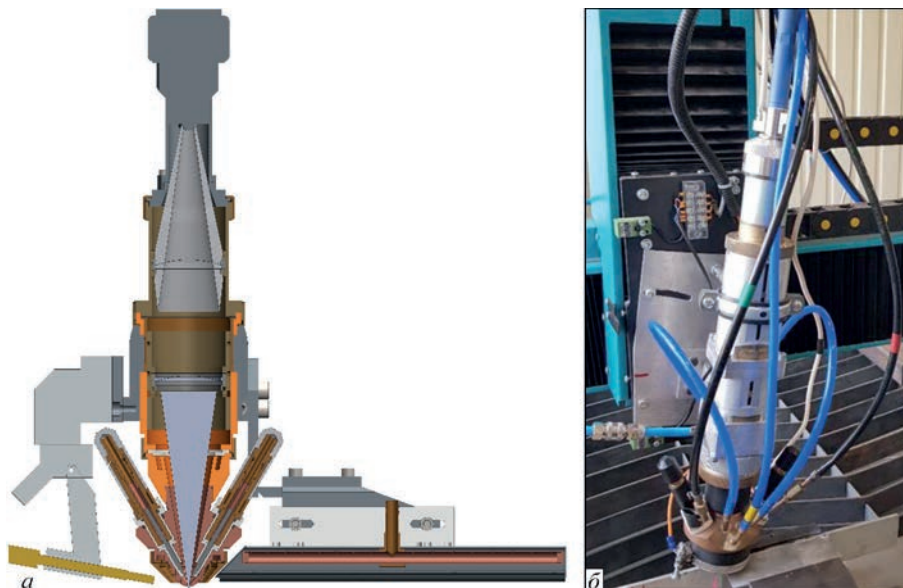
3D-модель (а) та зовнішній вигляд (б) головки для лазерного та лазерно-плазмового зварювання, розроблена в ІЕЗ ім. Є.О. Патона [46]
